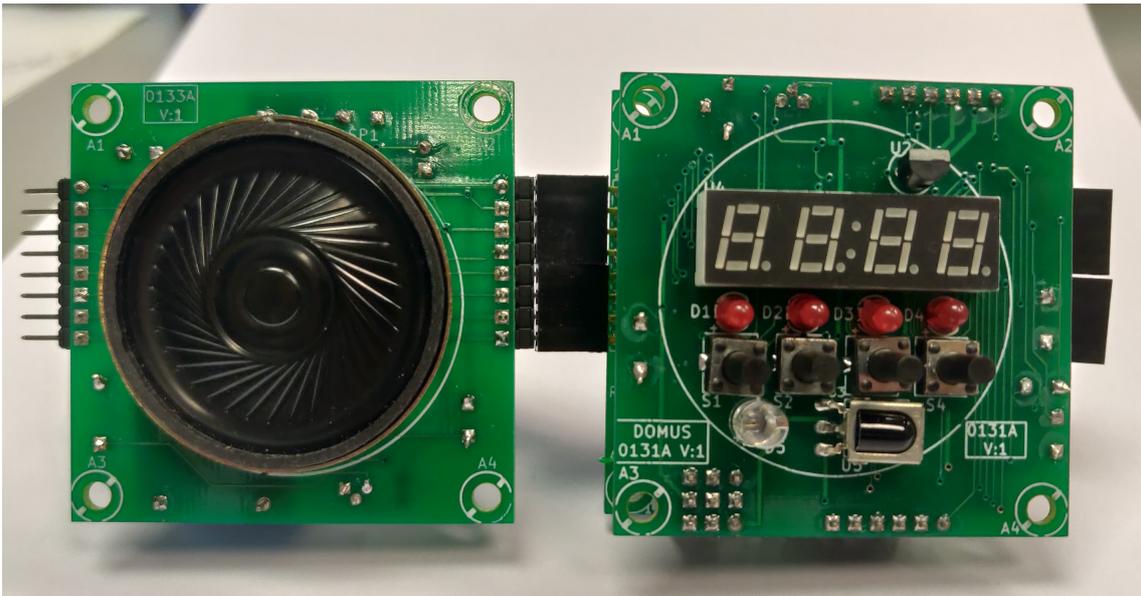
Vista frontal del montaje del sistema junto al Módulo de Control
